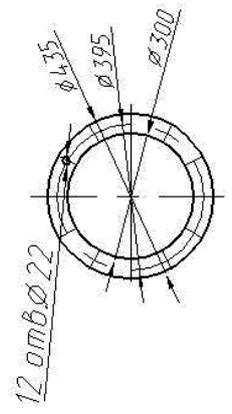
Габаритные размеры газодувки ТГ-65-1.06
